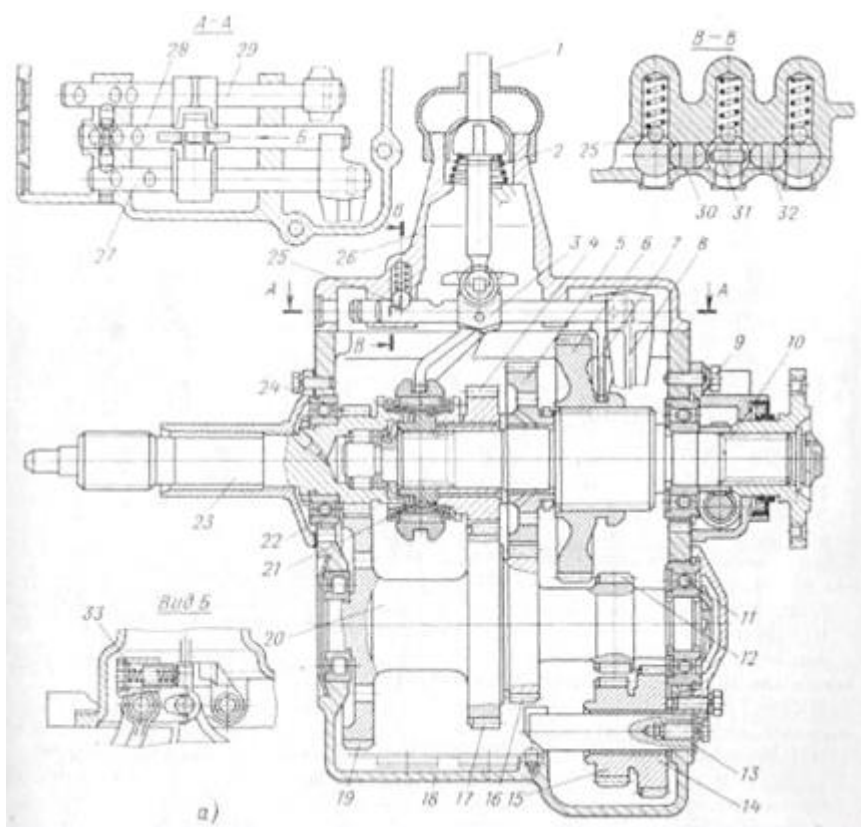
Коробка переміни передач: 1 - гайка; 2- кільце штопорне; 3 - підшипник; 4 - кільце синхронізатора; 5 - ролик 6x18; 6 - пружина синхронізатора; 7 - сухарик синхронізатора; 8 - муфта; 9 - штопор; 10 - втулка розпірна; 11 - втулка шестерні третьої передачі; 12 - шестерня третьої передачі в зборі; 13 - шайба; 14 - втулка шестерні другої передачі; 15 - шестерня другої передачі в зборі; 16 - шестерня ковна; 17 - вал вторинний;
